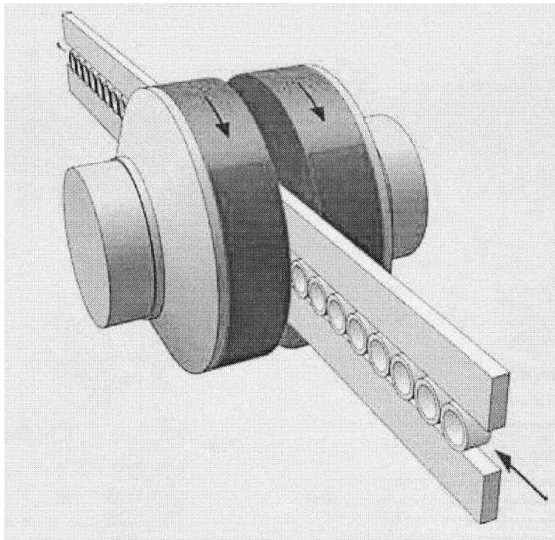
Шліфування з прямолінійним рухом оброблюваних заготовок
